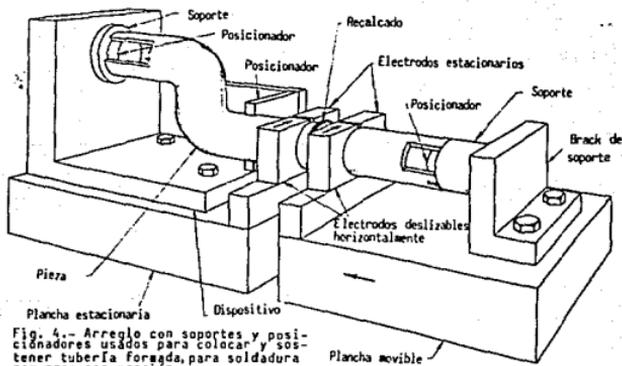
Arreglo con soportes y posicionadores usados para colocar y sostener tubería formada, para soldadura por arco con presión.
